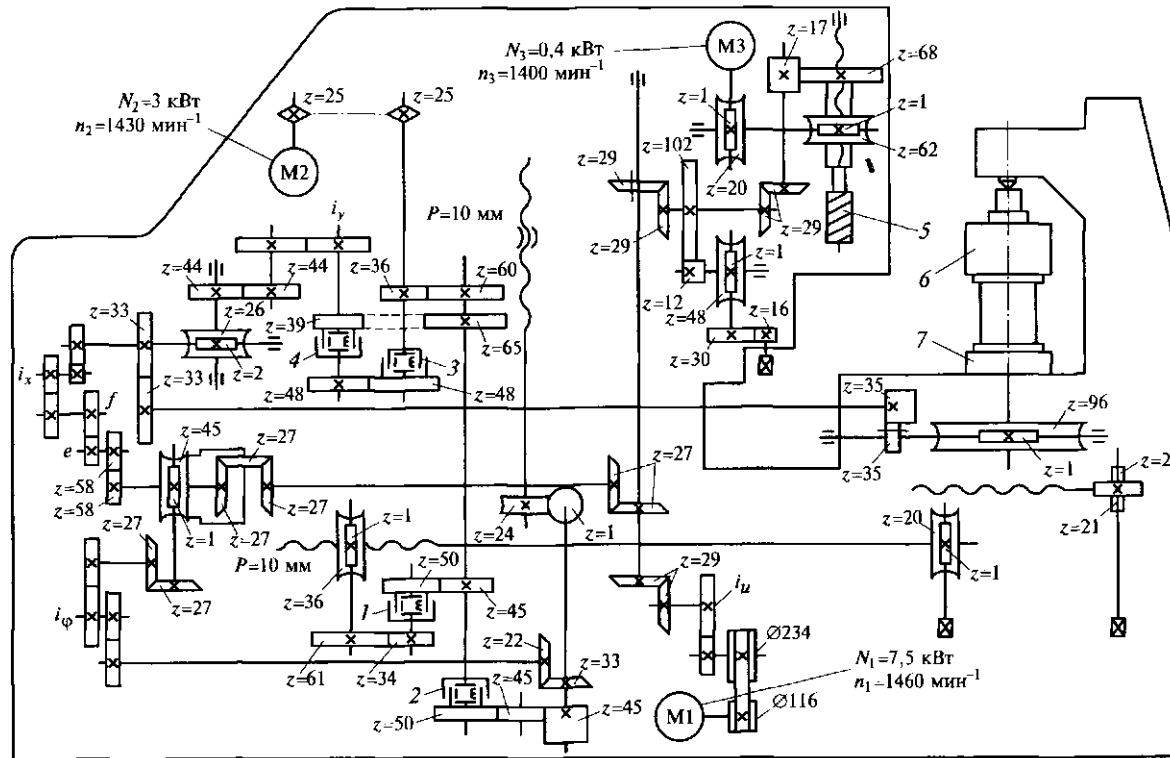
Кинематическая схема зубофрезерного станка:
